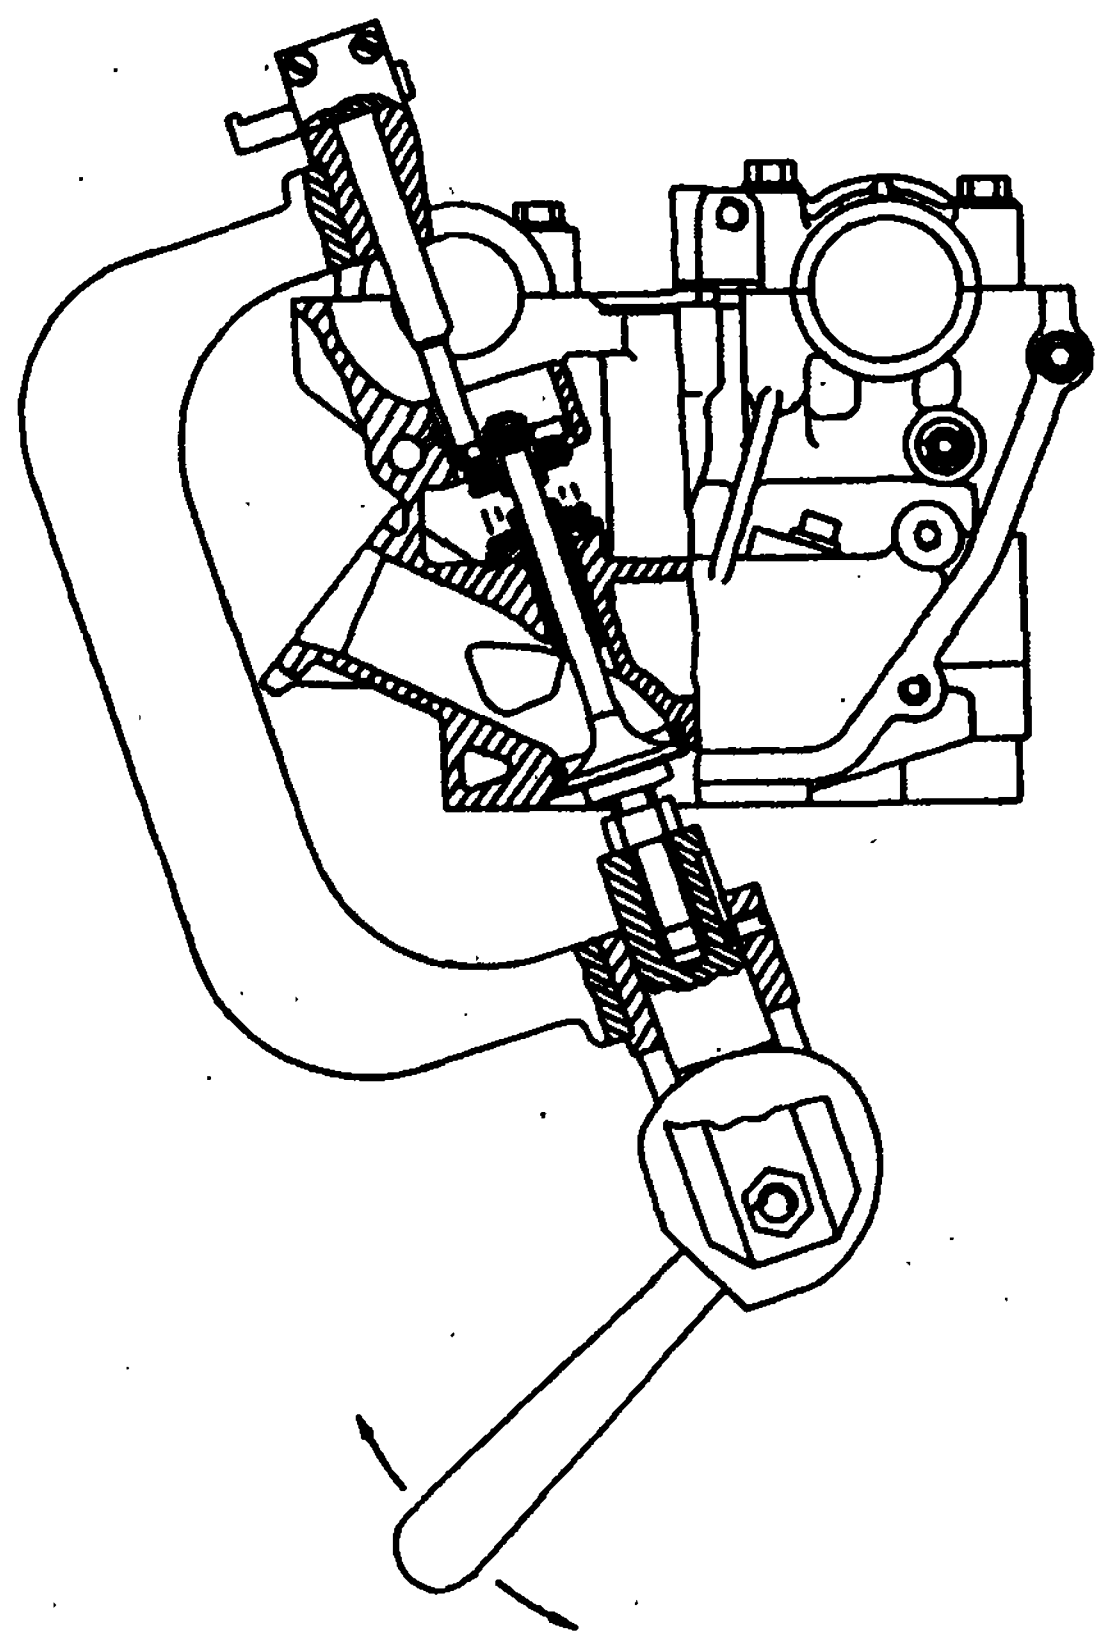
Снятие клапанных пружин с помощью приспособления ЗМ7814-5119
